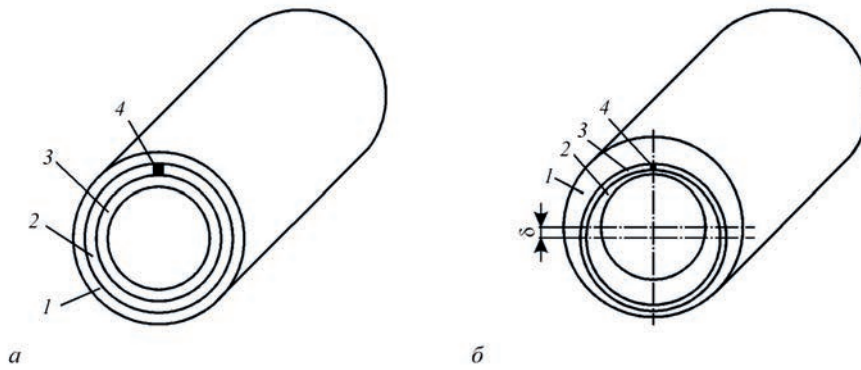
Однозначний дискретний (а) і багатозначний (б) СЗ складеного типу для імітації дефектів циліндричних ОК: 1–3 – шари циліндричного СЗ; 4 – ШД; δ – ексцентриситет
